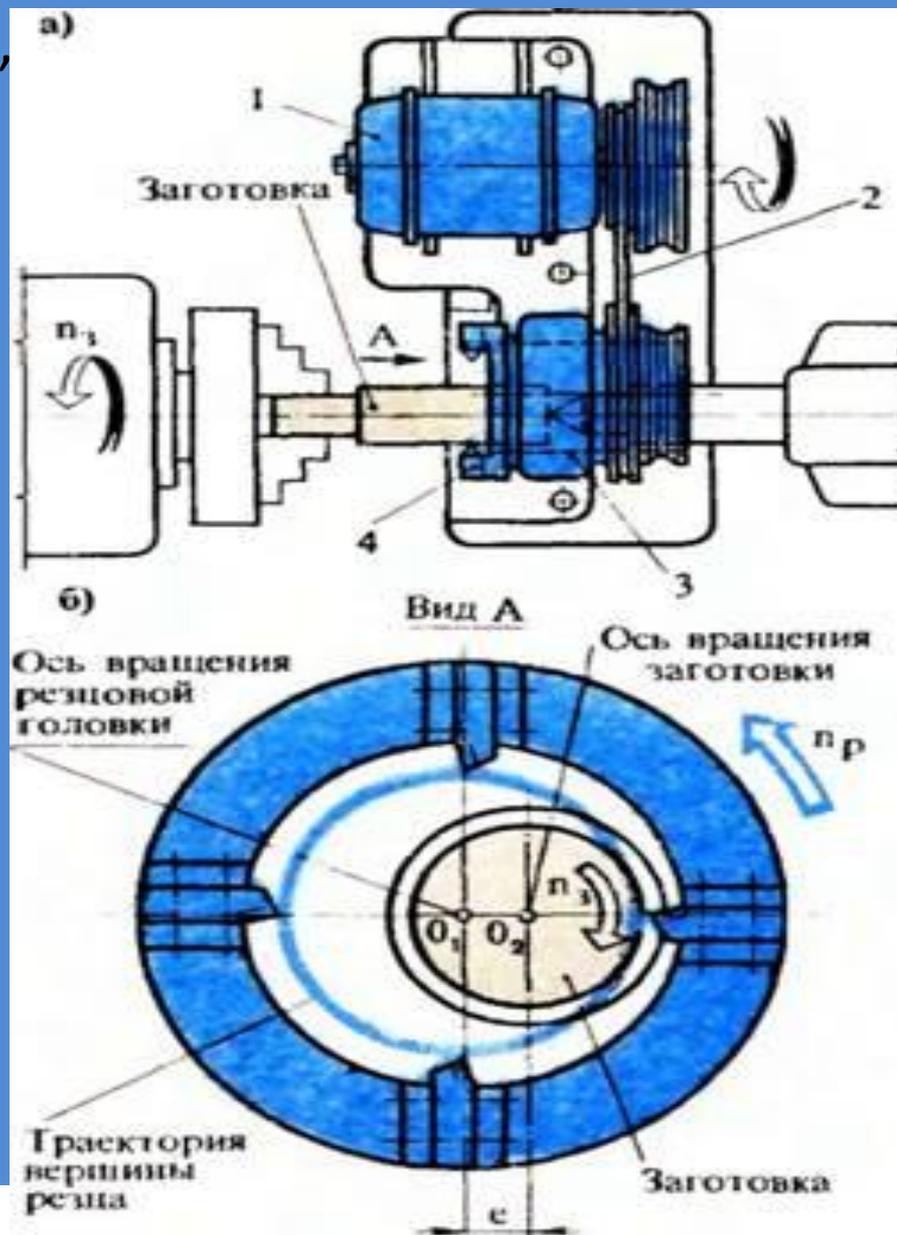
Схема нарезания внутренней резьбы вращающейся резцовой головкой
